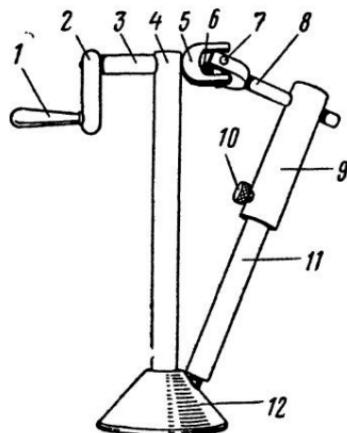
Модель карданной передачи: 1 — ручка; 2 — рычаг ручки; 3 — втулка; 4 — стойка; 5 — вал привода; 6 — крестовина; 7 — шип; 8 — ведомый вал; 9 — втулка; 10 — фиксатор; 11 — стойка; 12 — основание.
